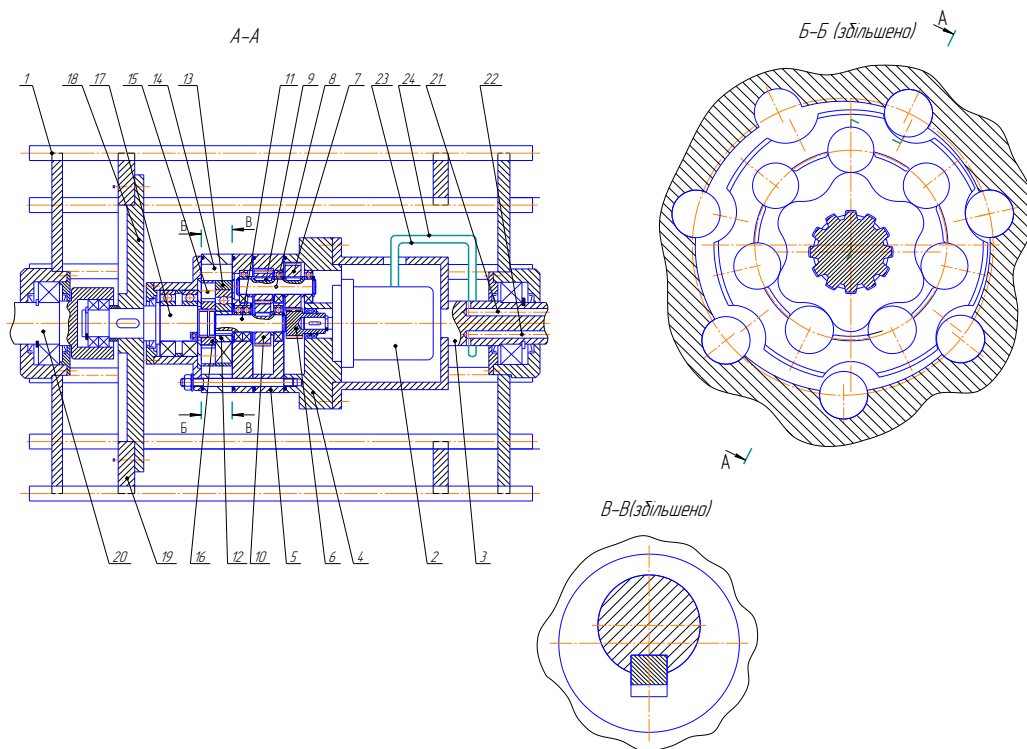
Конструкція гідравлічного вмонтованого привода з триступеневим редуктором укладального конвеєра
